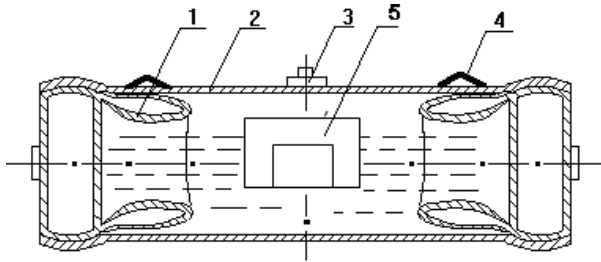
Схема резервуара з плаваючим в контейнері зразком озброєння (1 – допоміжні рукава; 2 – корпус резервуара; 3 – зливо-наливне пристосування; 4 – кріплення для переміщення резервуара; 5 – контейнер)
